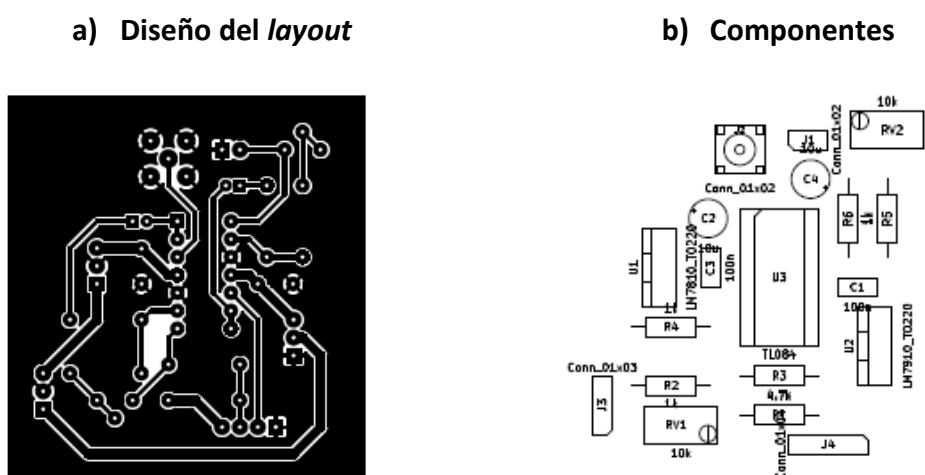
Diseño del layout (a) y componentes (b) de la PCB con dimensiones (ancho x alto): 50.8 x 54.6 mm
